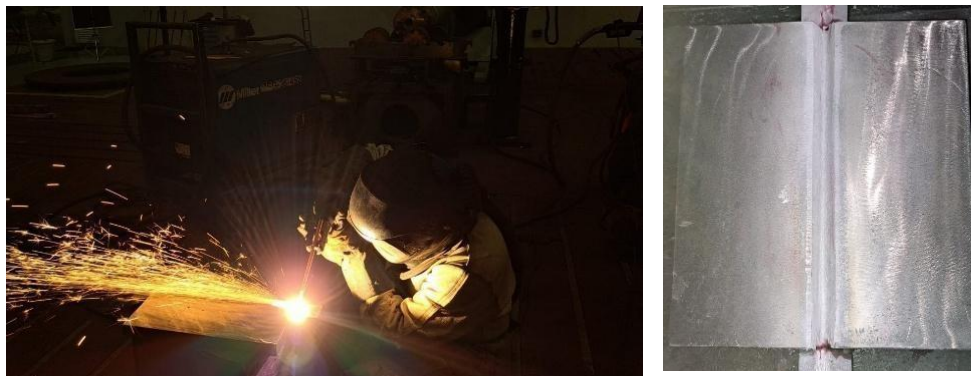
Conjuntos de corpos de prova preparados para soldagem com FCAW e SAW
